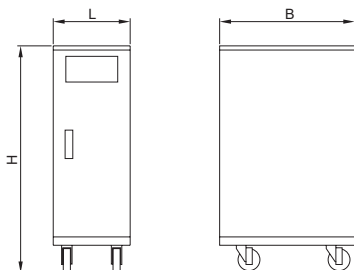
Габаритные размеры стабилизатора / Figure 1 – Overall dimensions of the stabilizer
